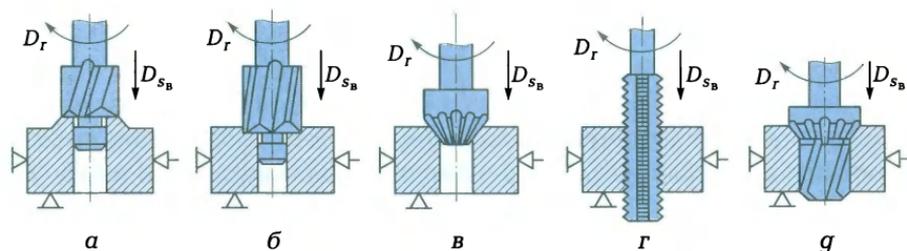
Схемы обработки заготовок на вертикально-сверлильном станке: а — цекование; б, в — зенкование; г — нарезание резьбы; г — комбинированная обработка;  $\nabla$  — неподвижная опора;  $\triangleleft$  — зажим
